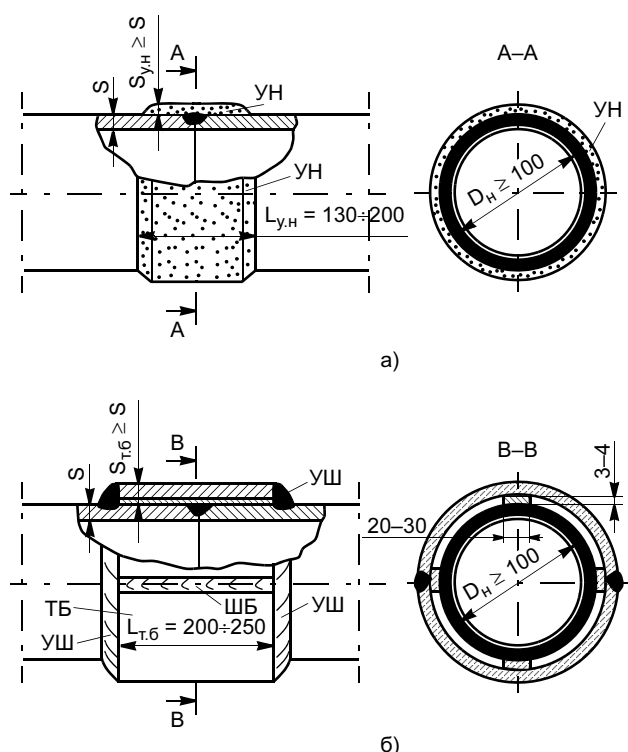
Укрепление ССС (ШБ — продольный шов бандаж, УШ — угловой): а — нанесение усиливающей наплавки (УН); б — приварка трубчатого бандаж (ТБ)
